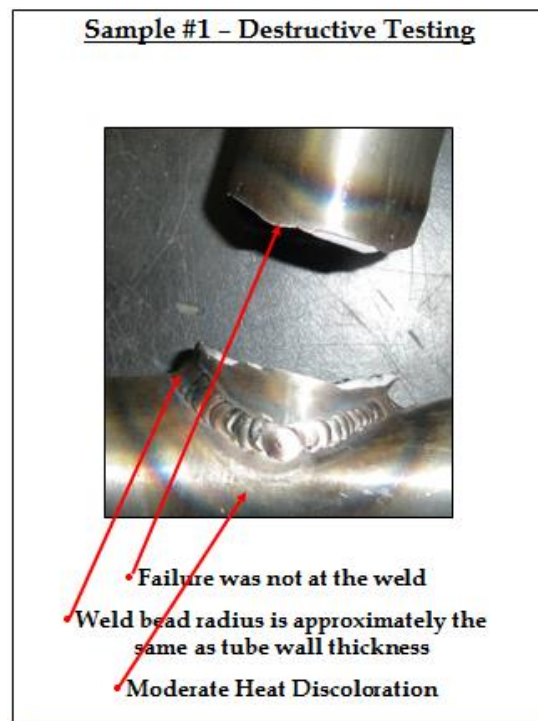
Prueba destructiva de soldadura válida [8]
